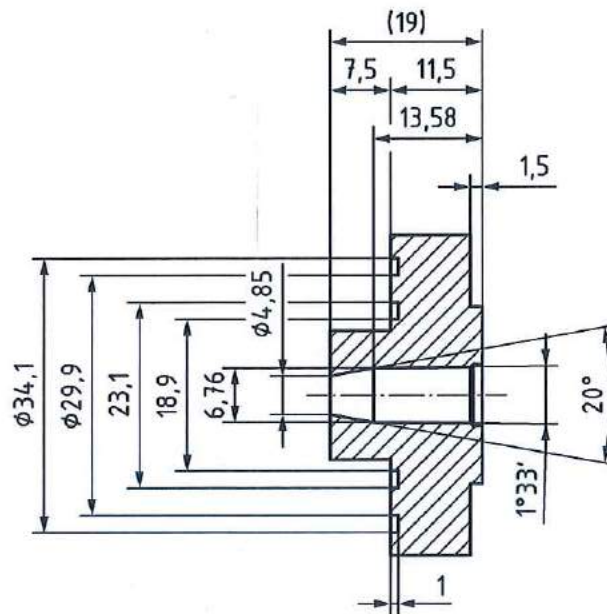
Insert de la chambre à cartouche pour Type 6,8/18
